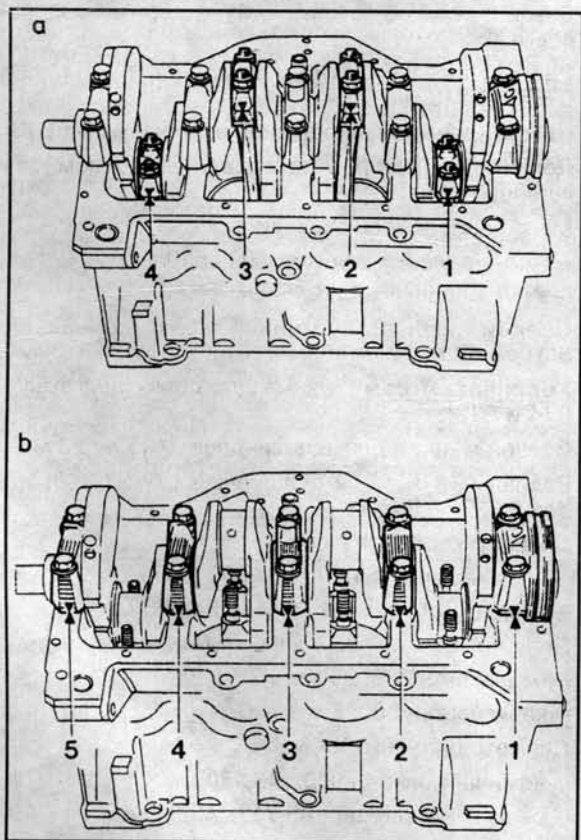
Способ нанесения меток на шатуны (а) и крышки коренных подшипников коленвала (б) в двигателях В13/В14
